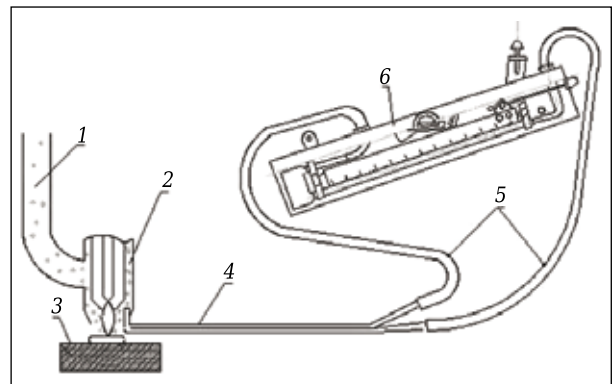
Схема измерения скорости газа: 1 — газопорошковая смесь; 2 — защитное сопло; 3 — наплавляемая деталь; 4 — трубка Пито – Прандтля; 5 — соединительные трубопроводы; 6 — тягонапормер
